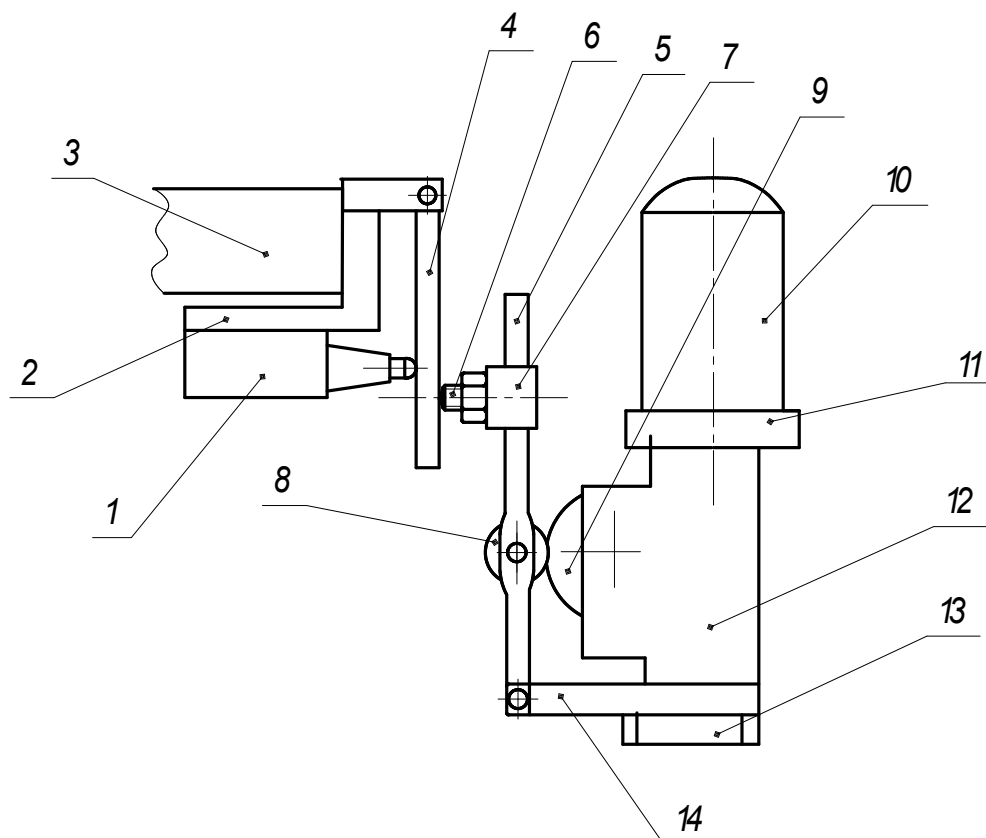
Додаткові пристрої для верстата моделі 5A27C1 при обробці западини зуба шестірні методами копіювання і обкатування
